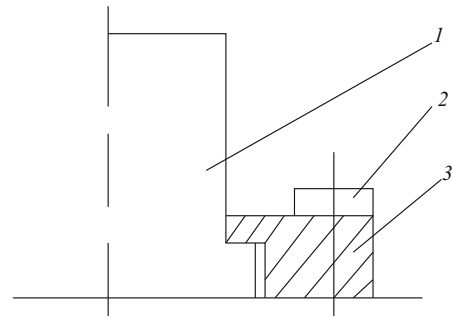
Фиксация гайки поршня РК по сборочному чертежу гидроагрегата:
